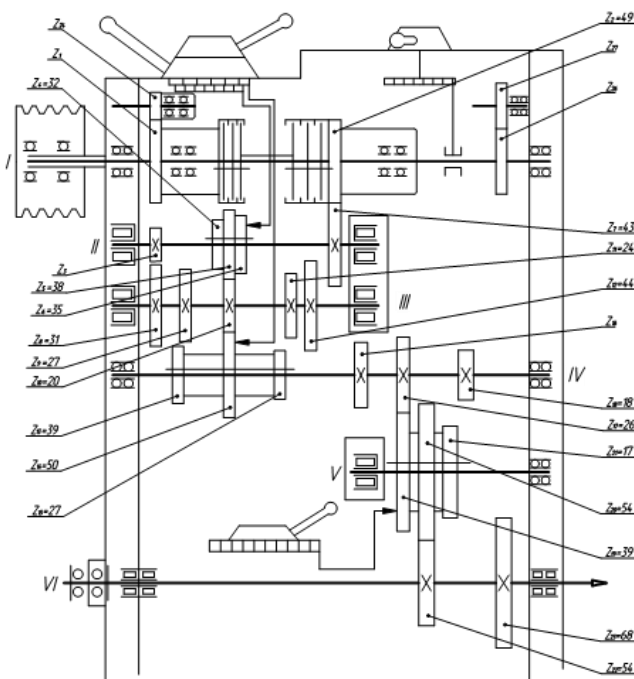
Кинематическая схема коробки скоростей привода главного движения токарного станка SN-401
